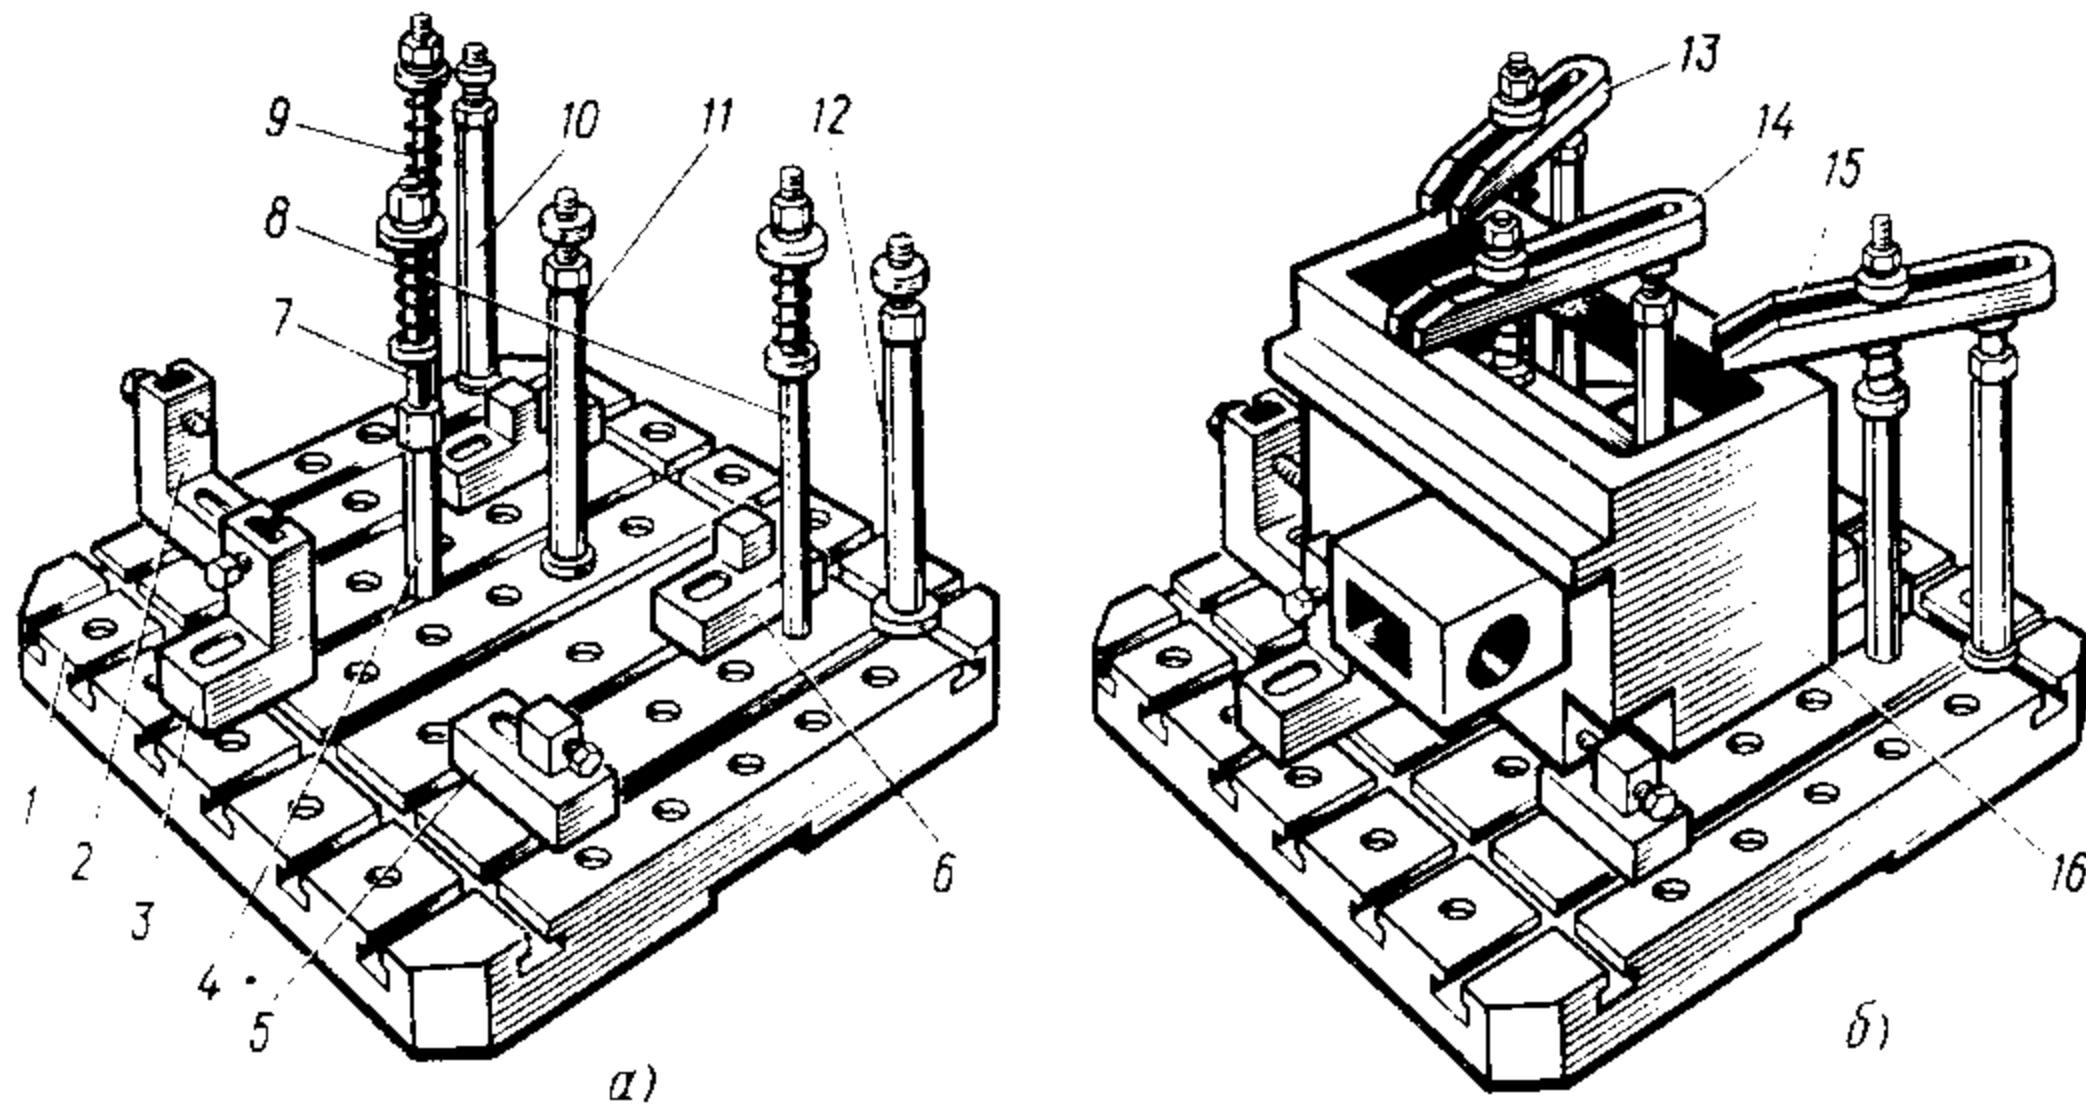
Устройство для закрепления заготовки на приспособлении-спутнике:
